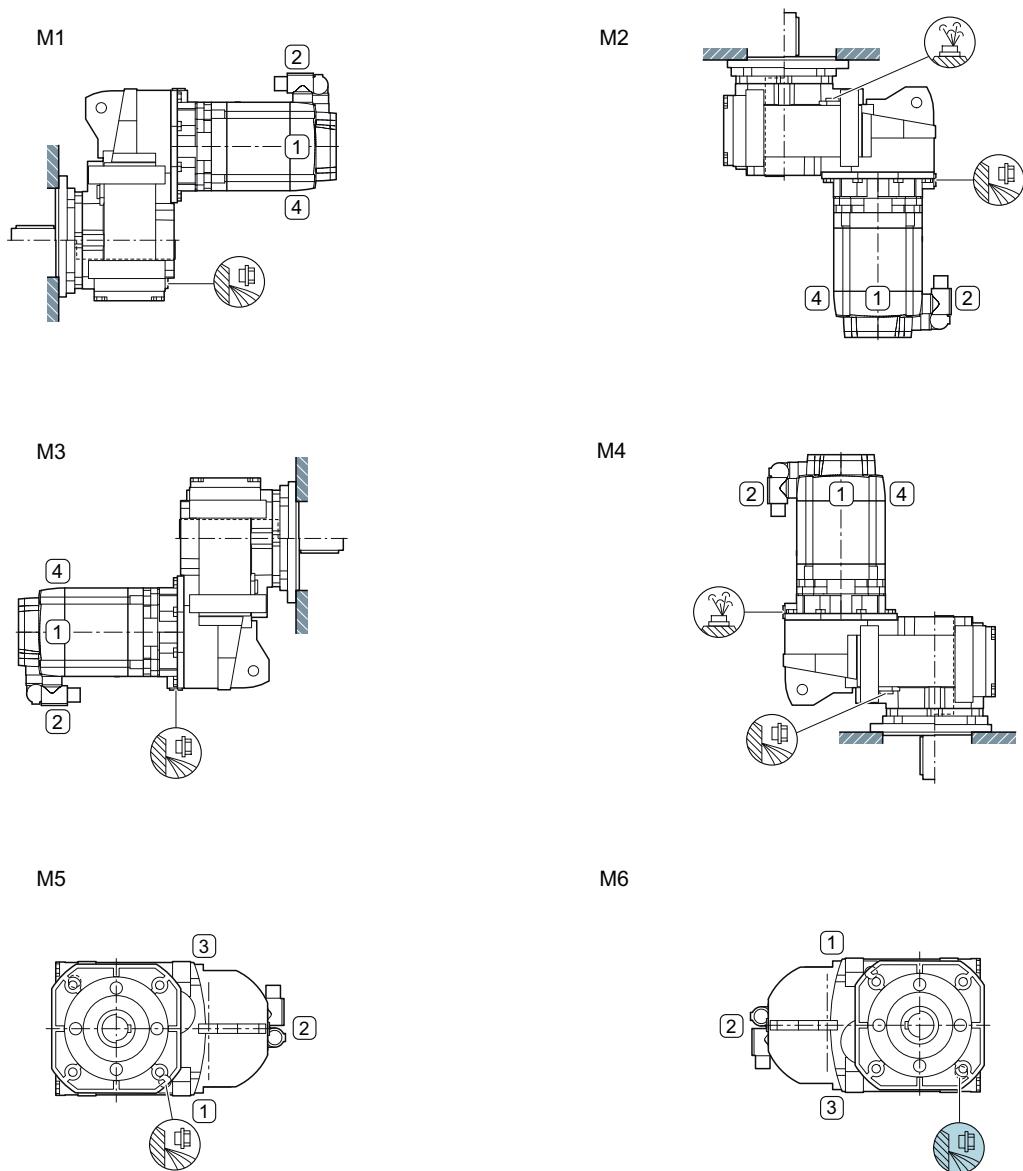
Einbaulagen für Servo-Flachgetriebemotoren FZ.F und FD.F (Flanschausführung) und FZ.Z und FD.Z (Gehäuseflanschausführung), Baugrößen 29, 2-stufig und 3-stufig
